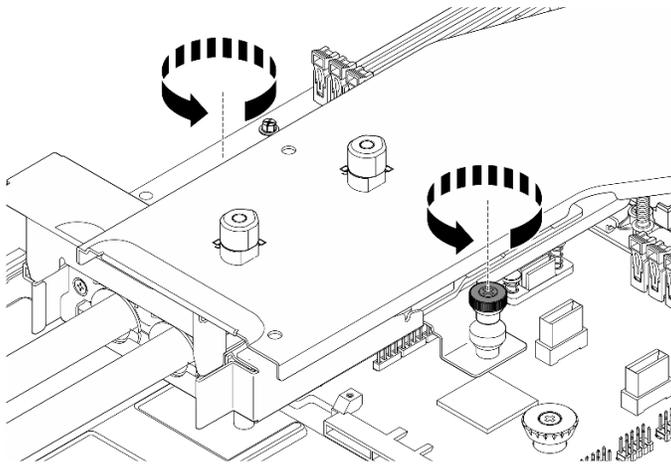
Entfernen der Kühlplattenbaugruppe
